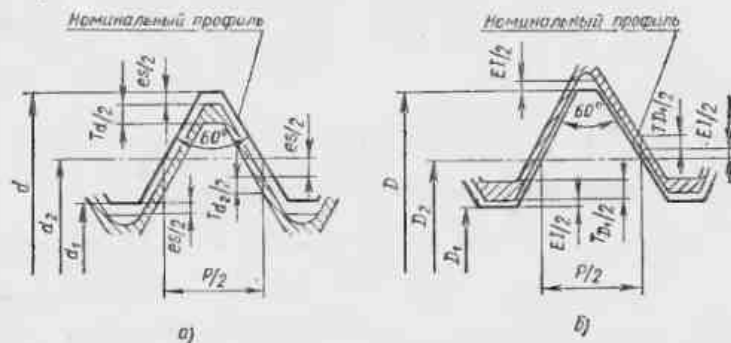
Расположение полей допусков резьбы при посадке с зазором: а — наружной; б — внутренней
